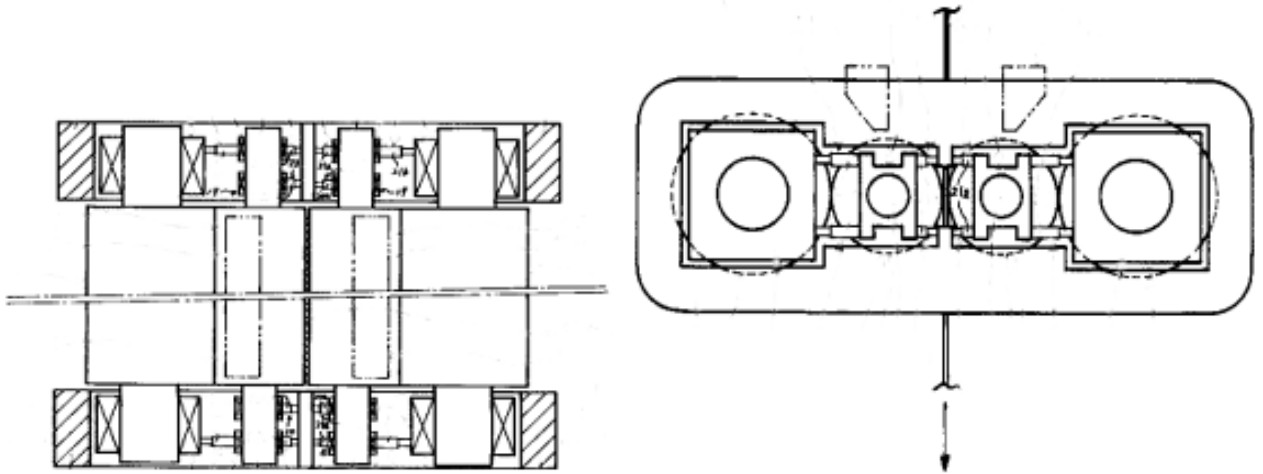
Схема рабочей клетки для прокатки порошков с системой противоизгиба рабочих валков.
